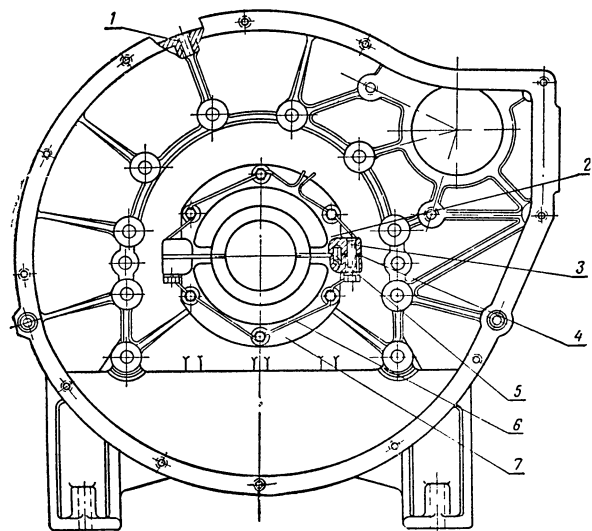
Задняя балка с корпусом уплотнения дизеля Д-54А:
